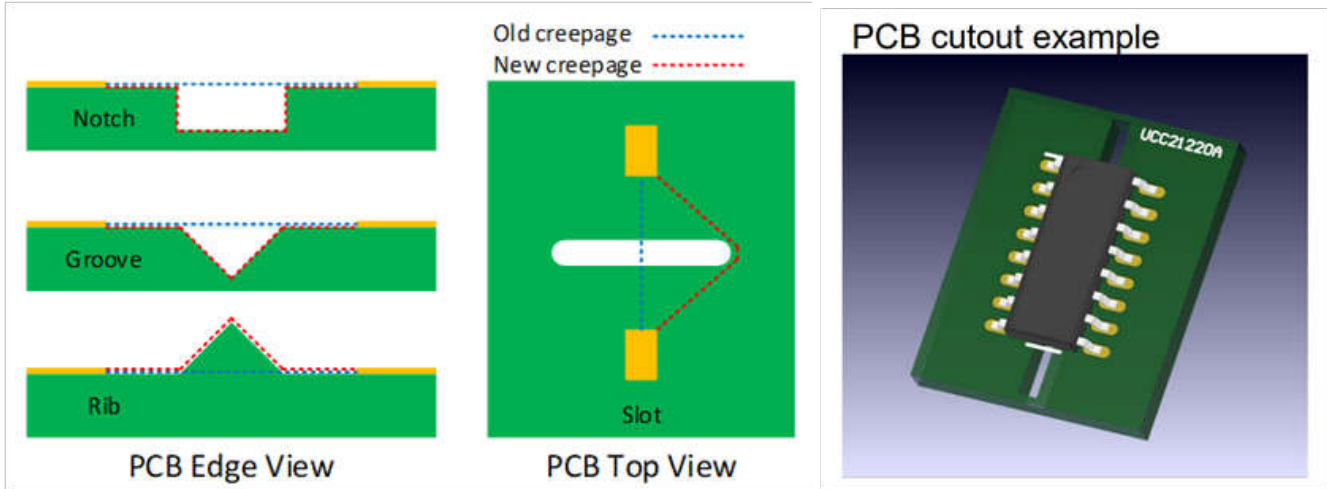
用于增加爬电距离的 PCB 开槽方法
